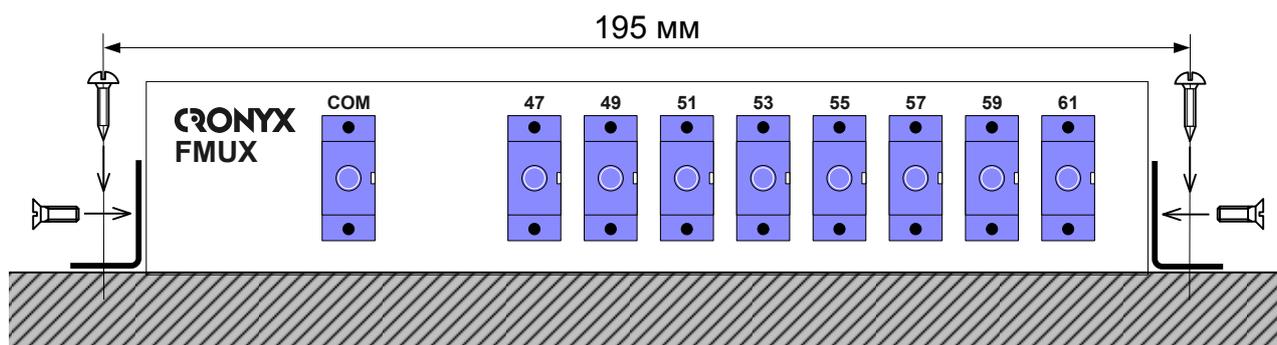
Крепление на стену, вид со стороны передней панели устройства
